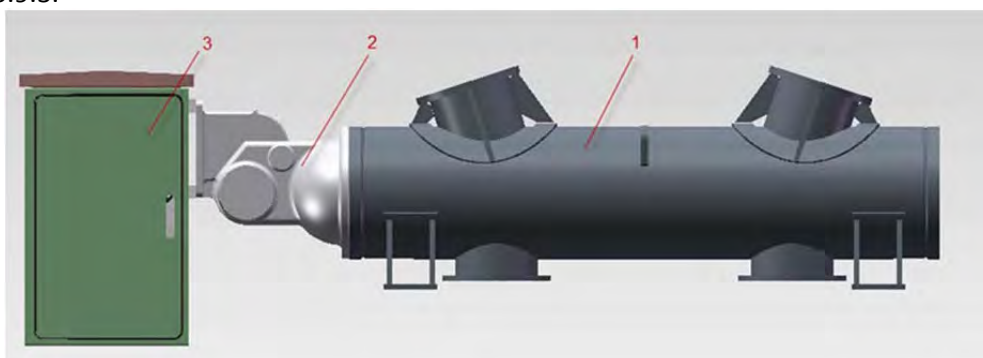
Внешний вид дугогасительного устройства
